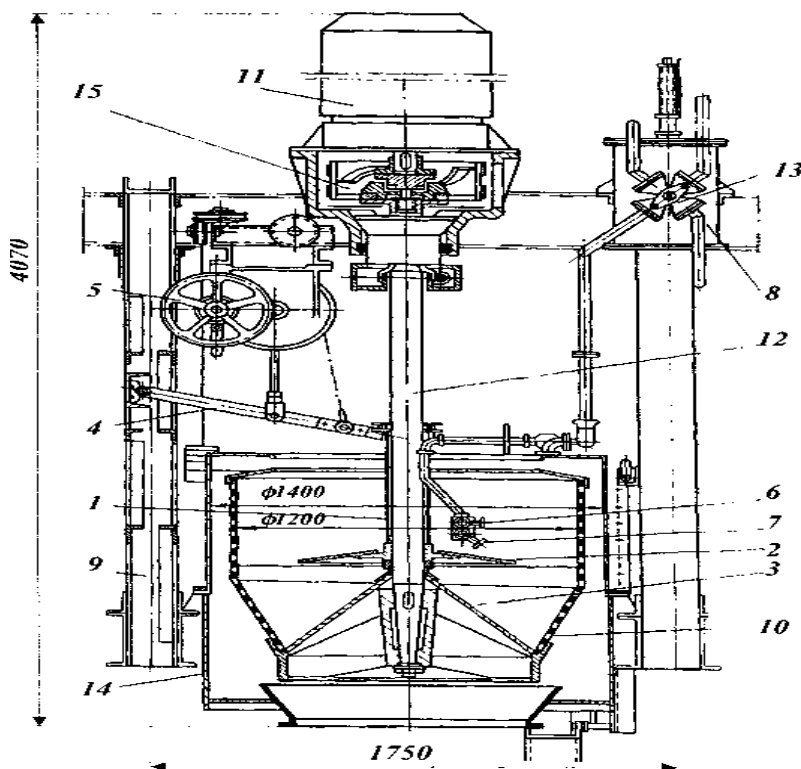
Фільтрувальна саморозвантажувальна центрифуга: 1 - муфта; 2 - тарілка; 3 - конус; 4 - ричаг; 5 - ручна лебідка; 6,7 - патрубки для пробілювання і пропарювання продукту; 8 - дозатор води; 9 - опорна конструкція; 10 - ротор; 11 - електродвигун; 12 - вал ротора; 13 - чотириходовий кран; 14 - кожух; 15 - шарнірна муфта.
